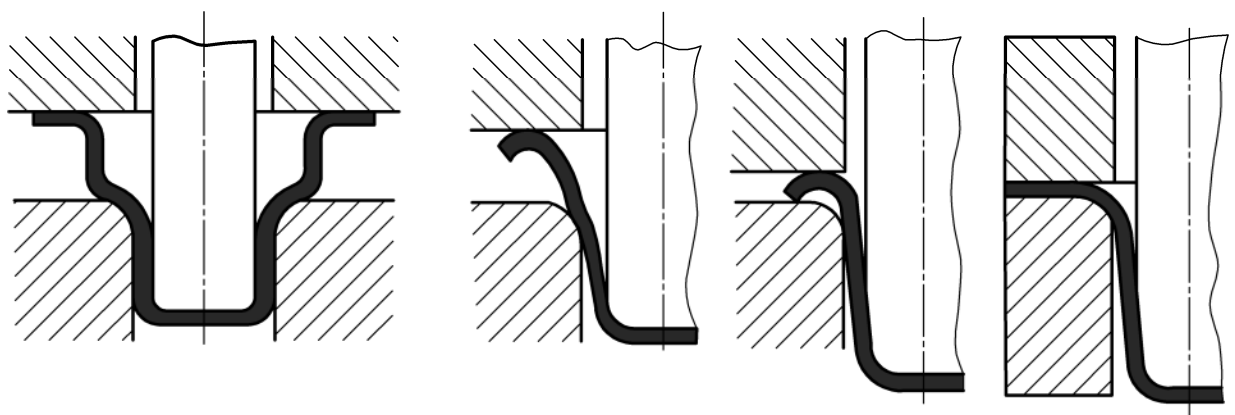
Схематичне зображення стадій формозміни під час витяжки та прошовхування деталі з широким фланцем
